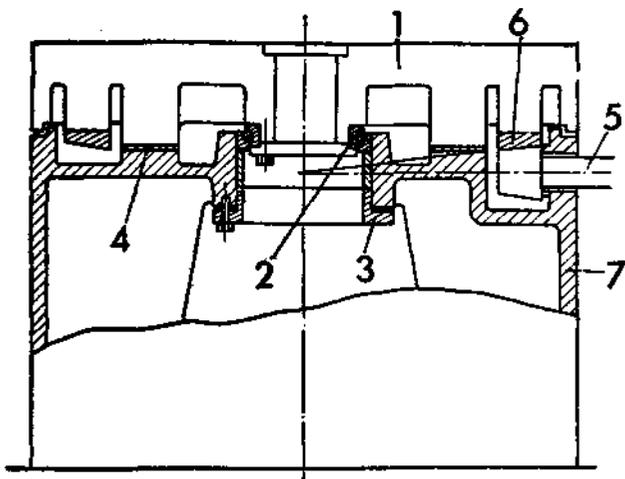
Esquema de montaje del eje principal sobre guía plana y rodamientos de rodillos cónicos: 1, plato; 2, rodamiento de rodillos (centraje); 3, cosquillo de reglaje; 4, guía plana, cubierta de antifricción; 5, piñón de ataque de la caja de velocidades; 6, corona dentada fija al plato; 7, banco.
